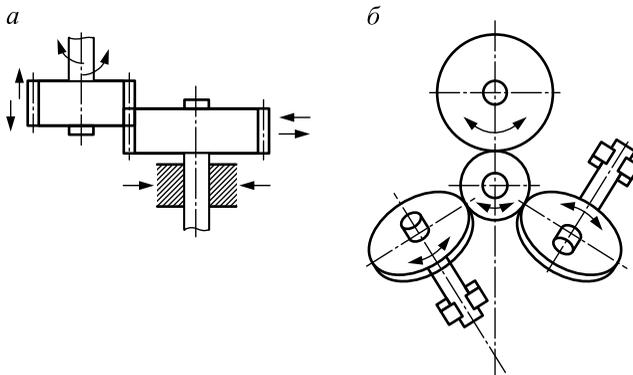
Схемы притирки зубьев цилиндрических зубчатых колес
